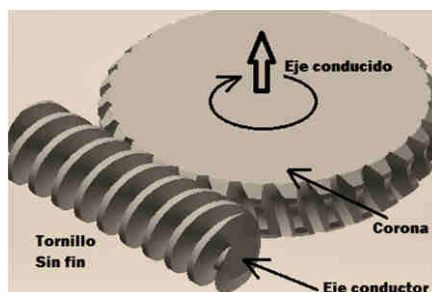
Diseño CAD de mecanismo tornillo sin fin – corona
